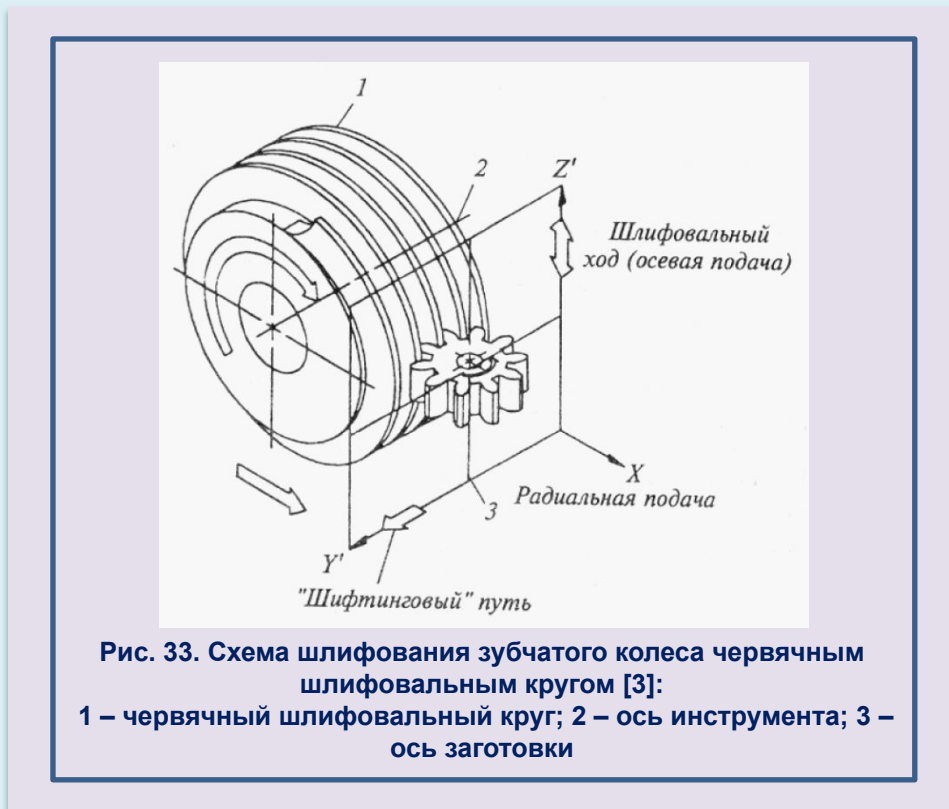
Схема шлифования зубчатого колеса червячным шлифовальным кругом [3]:
